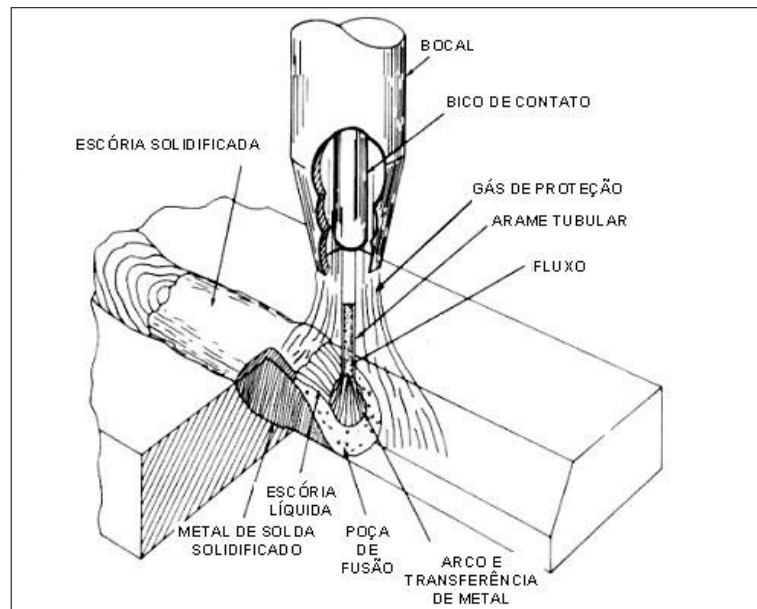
O processo de soldagem com eletrodos tubulares com gás de proteção (FORTES, 2004)
